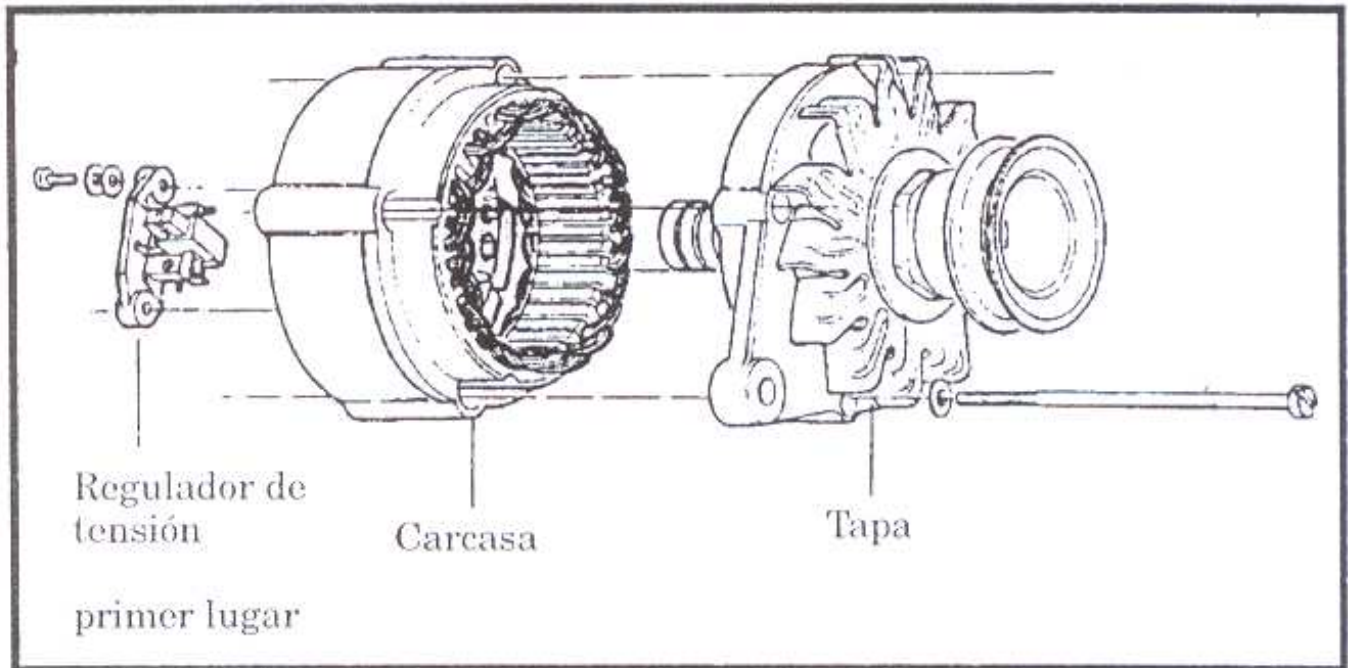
Desmontaje de la parte trasera del alternador.
